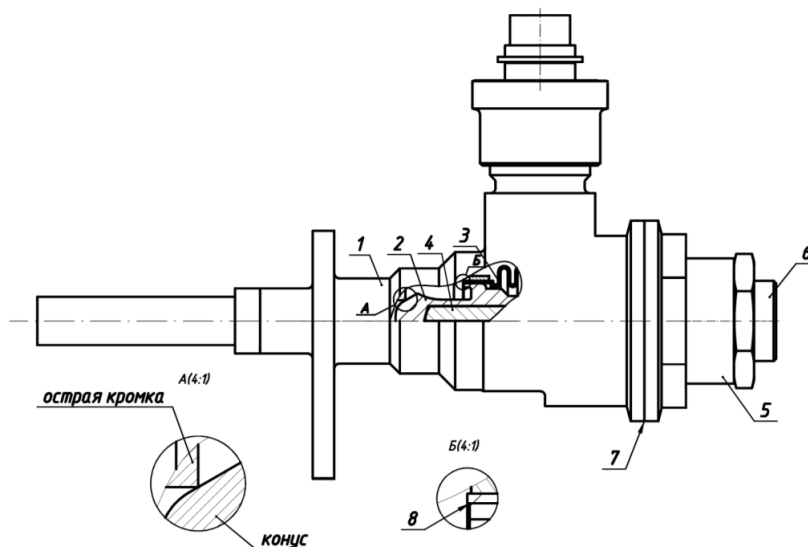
Вентиль № 1 заправочный: 1 – корпус; 2 – клапан; 3 – сильфон; 4 – стержень; 5 – втулка резьбовая; 6 – ручка; 7 – сварной шов; 8 – электронно-лучевая сварка многослойного торцевого шва (выносной элемент Б)
